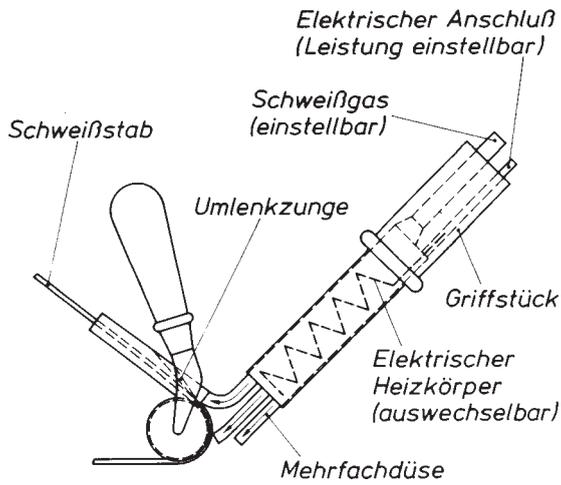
Schnellschweißgerät mit Mehrfachdüse und Andrückkrolle (schematisch)
